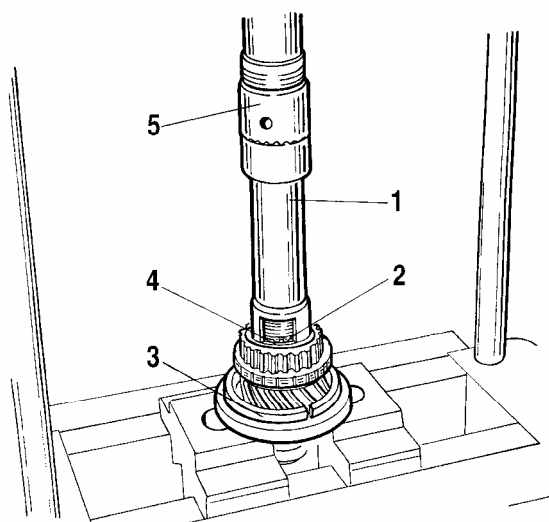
Установка на вторичном валу стопорного кольца:
